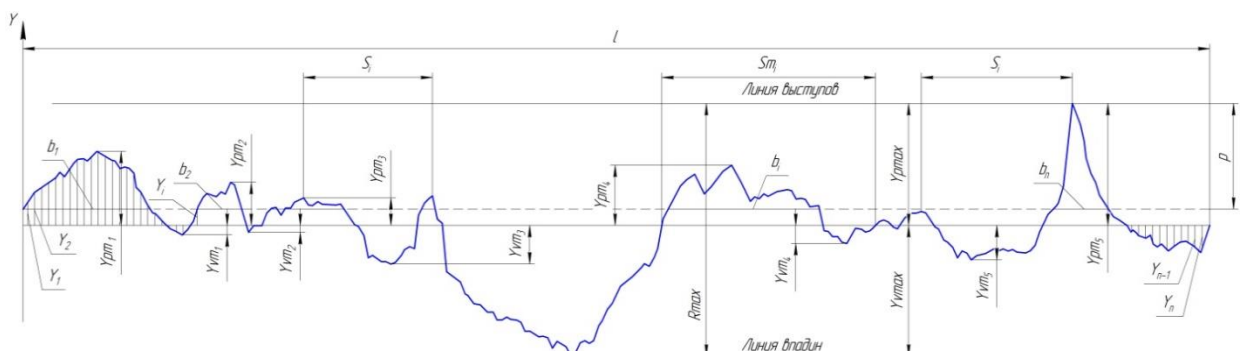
Параметры, описывающие шероховатость поверхности
